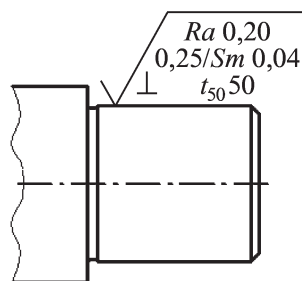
Обозначение параметров шероховатости на рабочей поверхности опорной шейки вала
